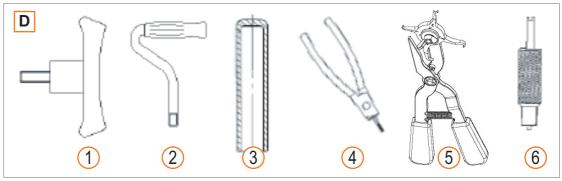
Werkzeugsatz 2480.00.50.11
